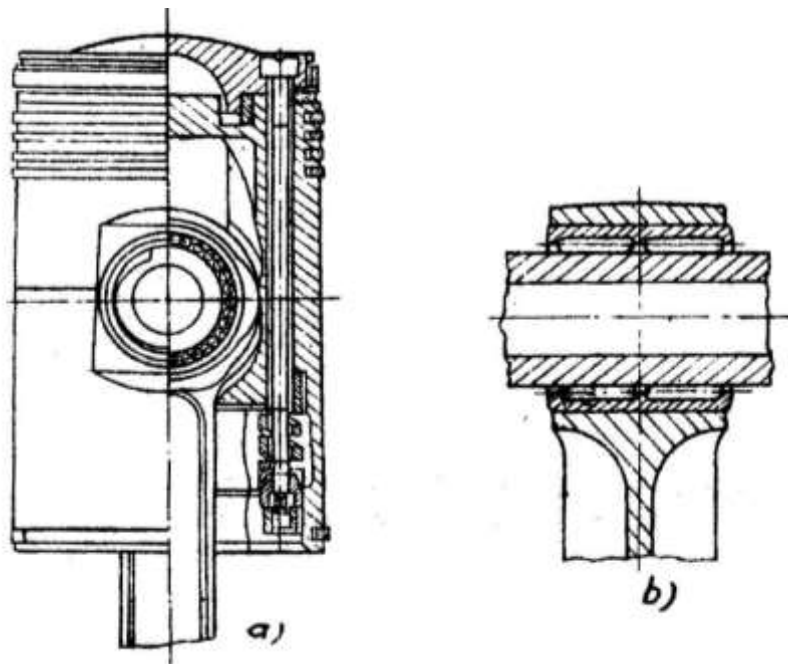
Bố trí lỗ hứng dầu trên đầu nhỏ thanh truyền
